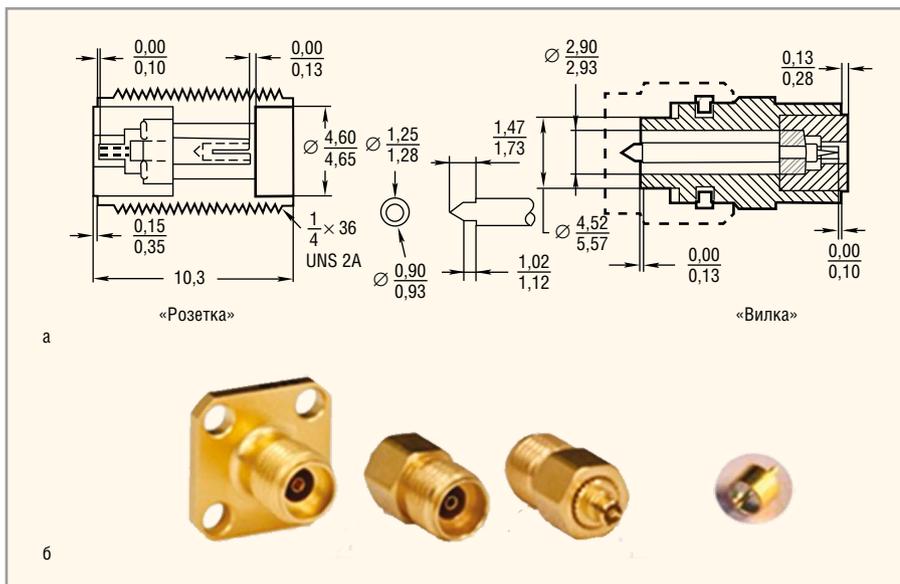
Резьбовой соединитель К: а – интерфейс; б – внешний вид
